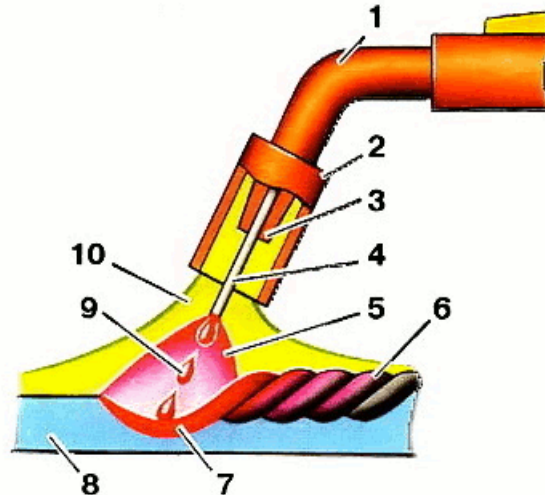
Схема полуавтоматической дуговой сварки
